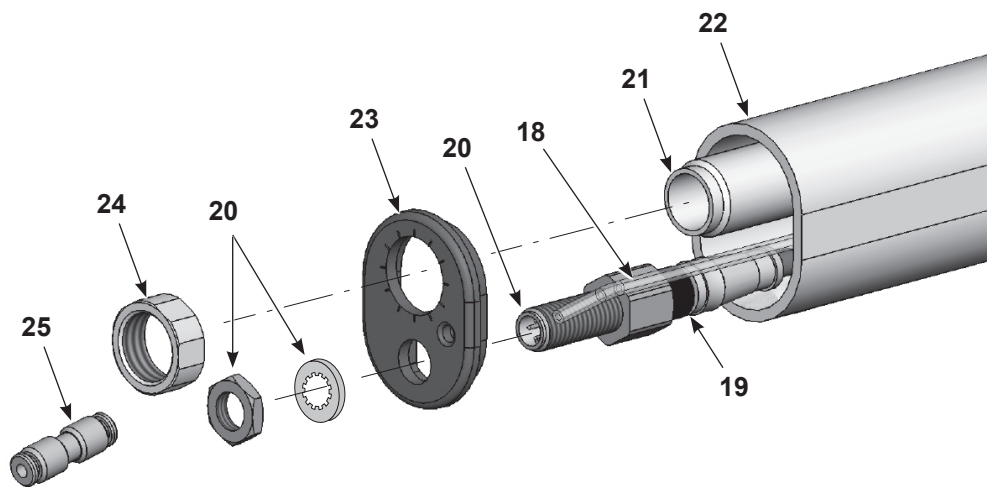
Démontage du pistolet à fixation sur tube 1 sur 5
